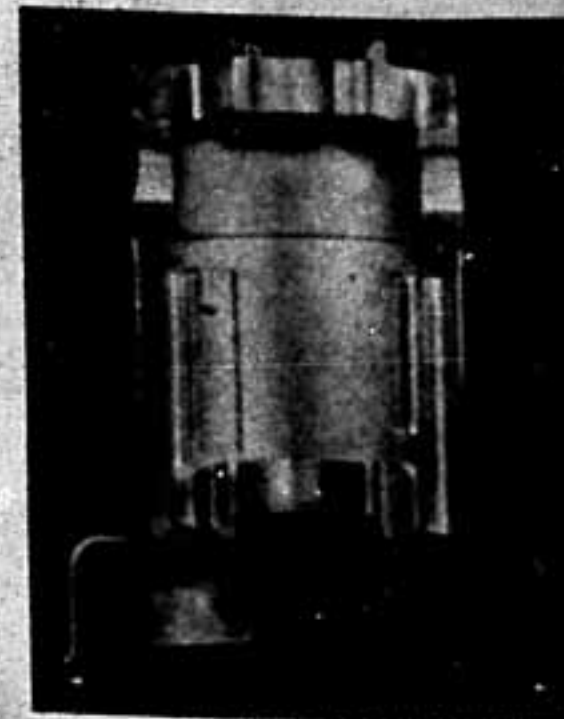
Motorgehäuse und Lagerschild für Staubsauger. Die beiden seitlichen Bohrungen des Lagerschildes sind mit einer Rudge-Vorrichtung versehen.
